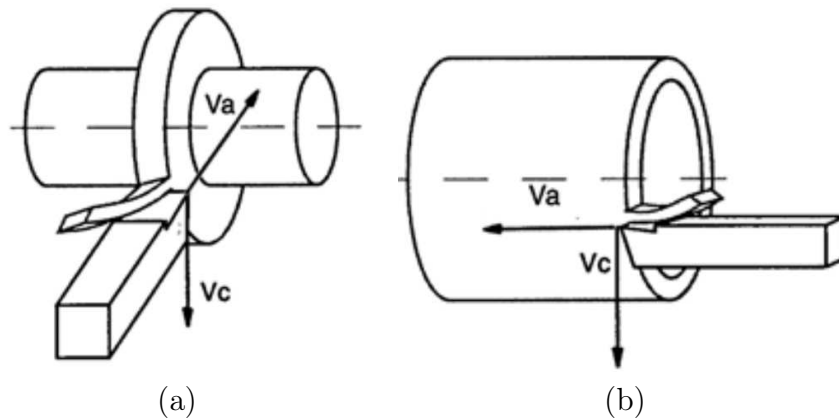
Configurations de la coupe orthogonale : (a) usinage d'un palier, (b) usinage d'un tube
